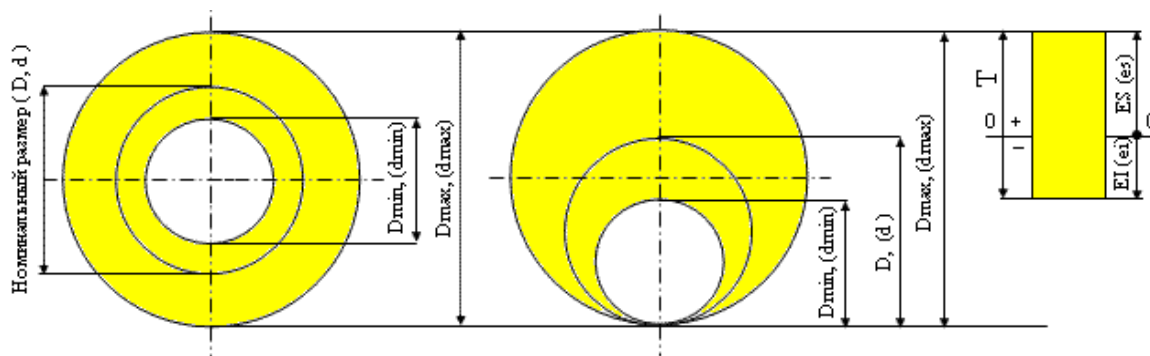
Поле допуска (T) для общего случая
